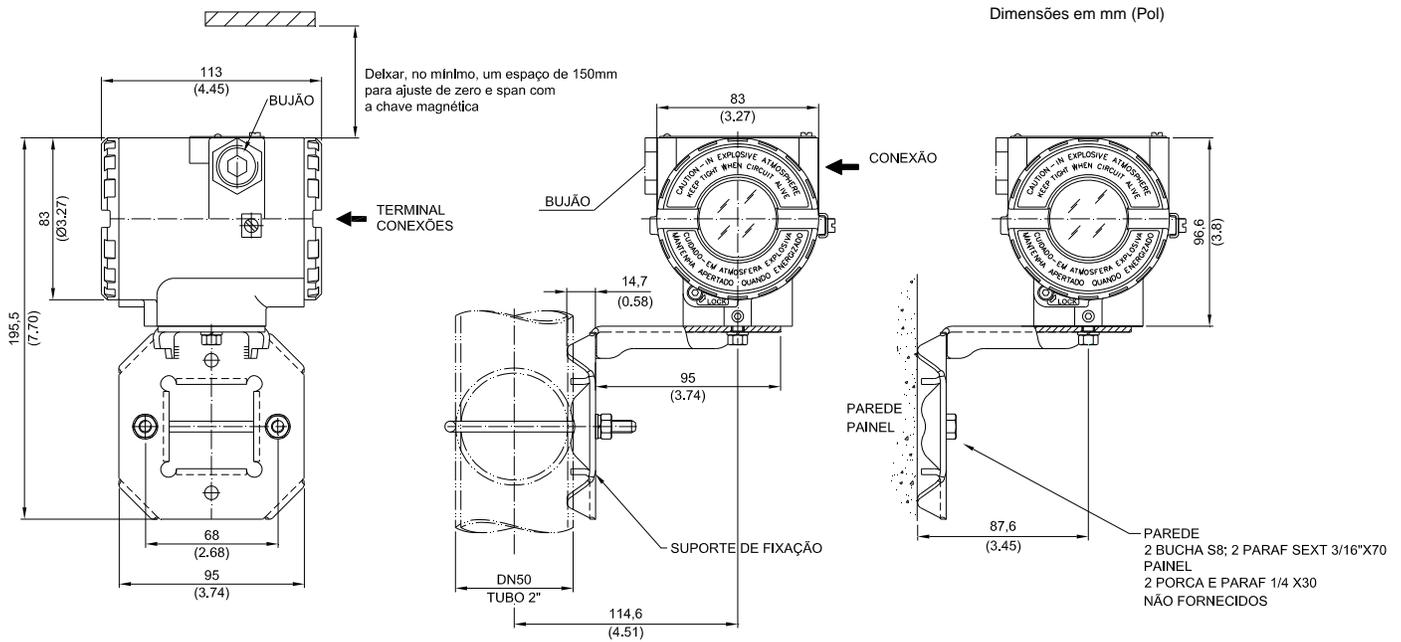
Posições de Montagem e Desenho Dimensional
